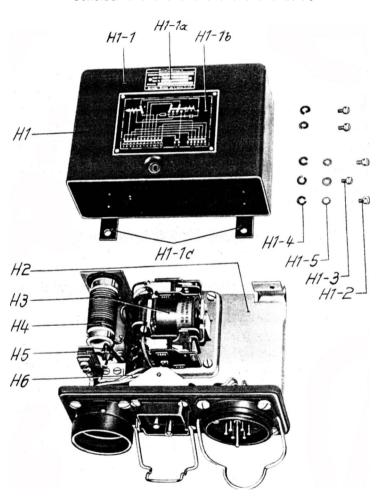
EDSK-B, Gruppen und Teile des Gehäuses (H 1)
